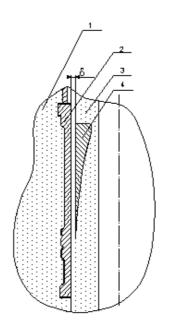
Схема отливки в песчано-глинистую форму втулки цилиндра судового дизеля с пассивным холодильником:
